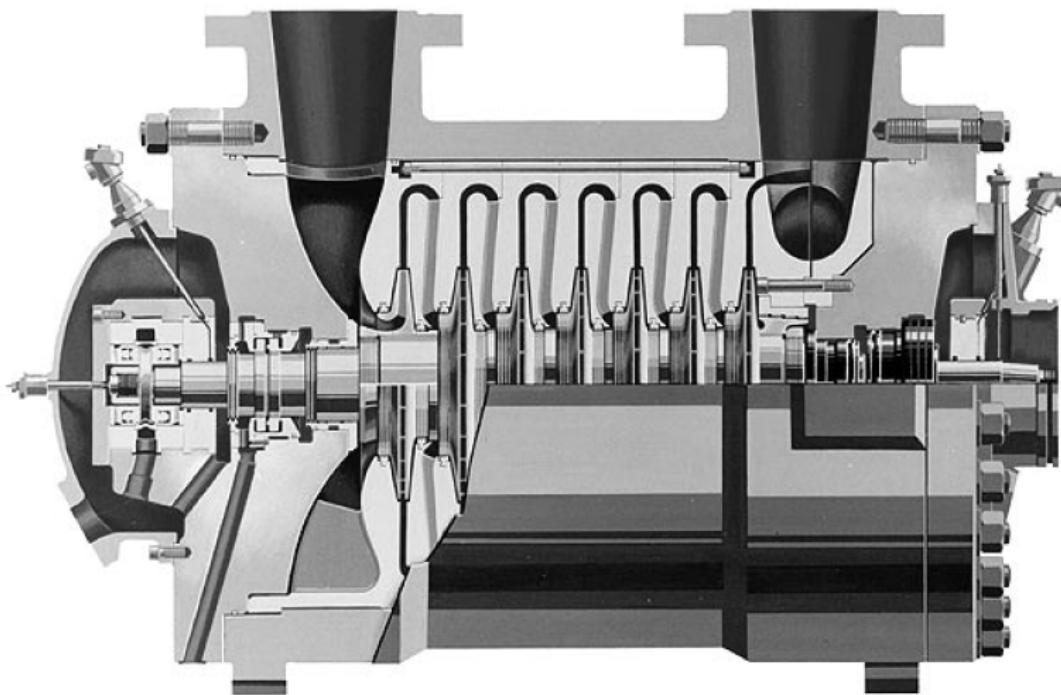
Compressor do tipo “barril” de múltiplos estágios e um estágio de compressão (Fonte: Compressor Handbook, Paul C. Hanlon)
